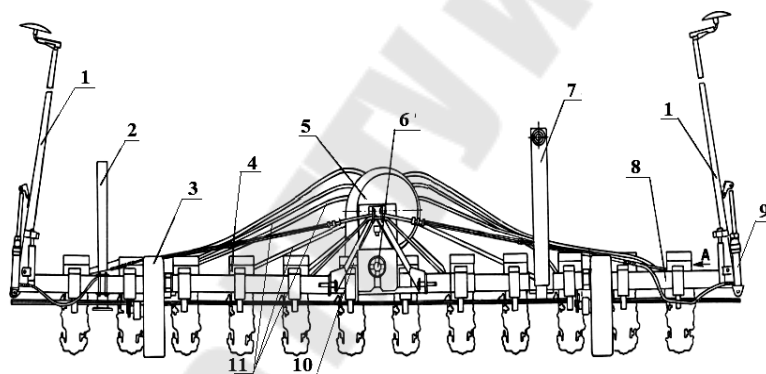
Общий вид сеялки СТВ-12: 1 – маркеры; 2 – стойка; 3 – колесо опорно-приводное; 4 – секция посевная; 5 – вентилятор; 6 – вал карданный; 7 – опора транспортного устройства; 8 – рама; 9 – гидроцилиндр; 10 – замок автосцепки; 11 – воздухопровод
